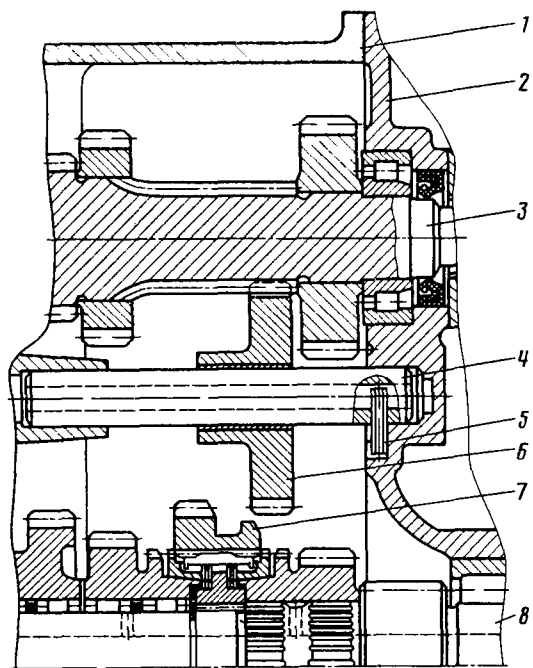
Промежуточная шестерня заднего хода коробки передач:
